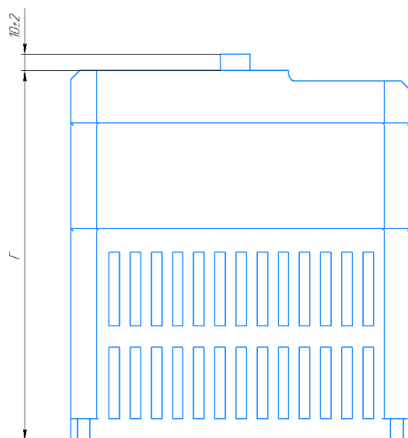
б - габаритные и установочные размеры устройств серии LCI в пластмассовом корпусе
